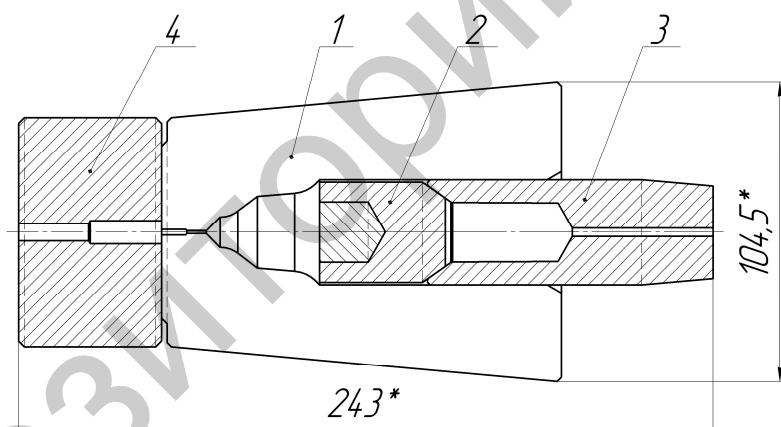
Внешний вид экспериментальной оснастки для изготовления резцов
